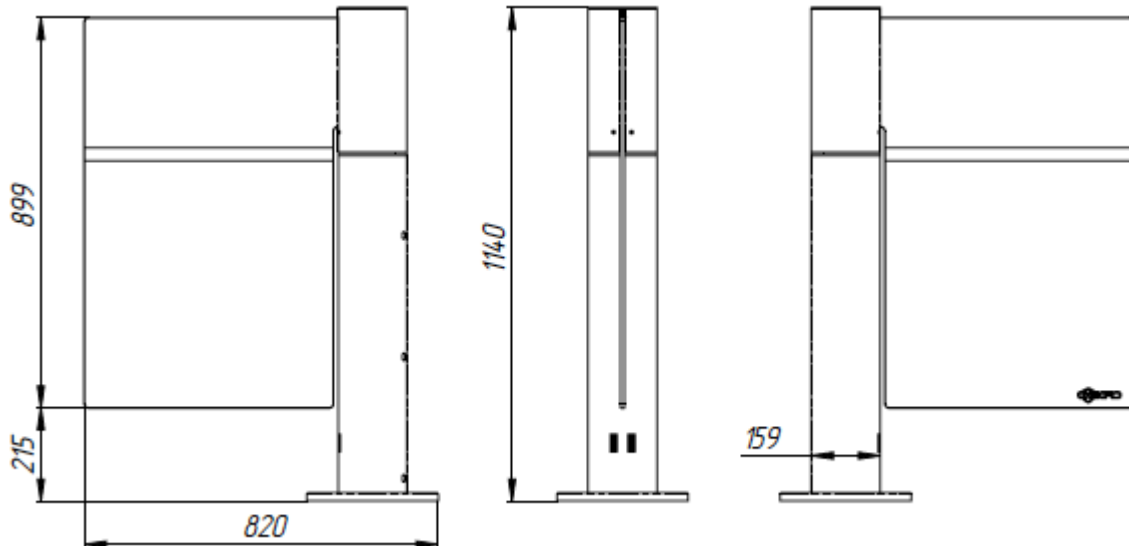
Габаритные размеры калитки шириной прохода 600 мм
